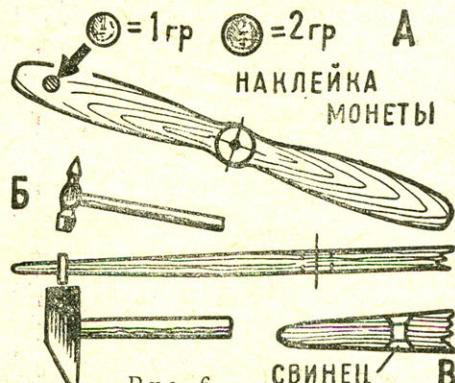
Балансировка винта путем вклепывания кусочков свинца:
